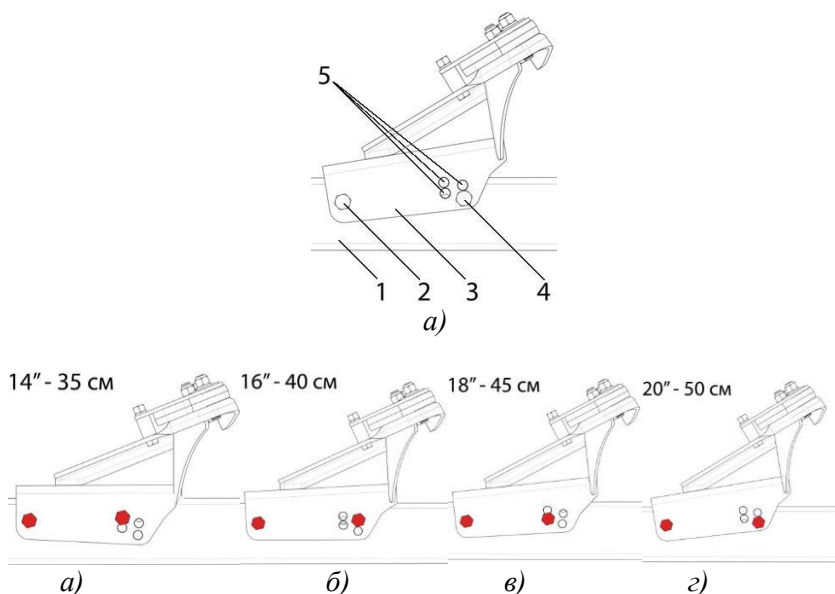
Схема установки кронштейна кріплення корпуса плуга при регулюванні його ширини захвату:
